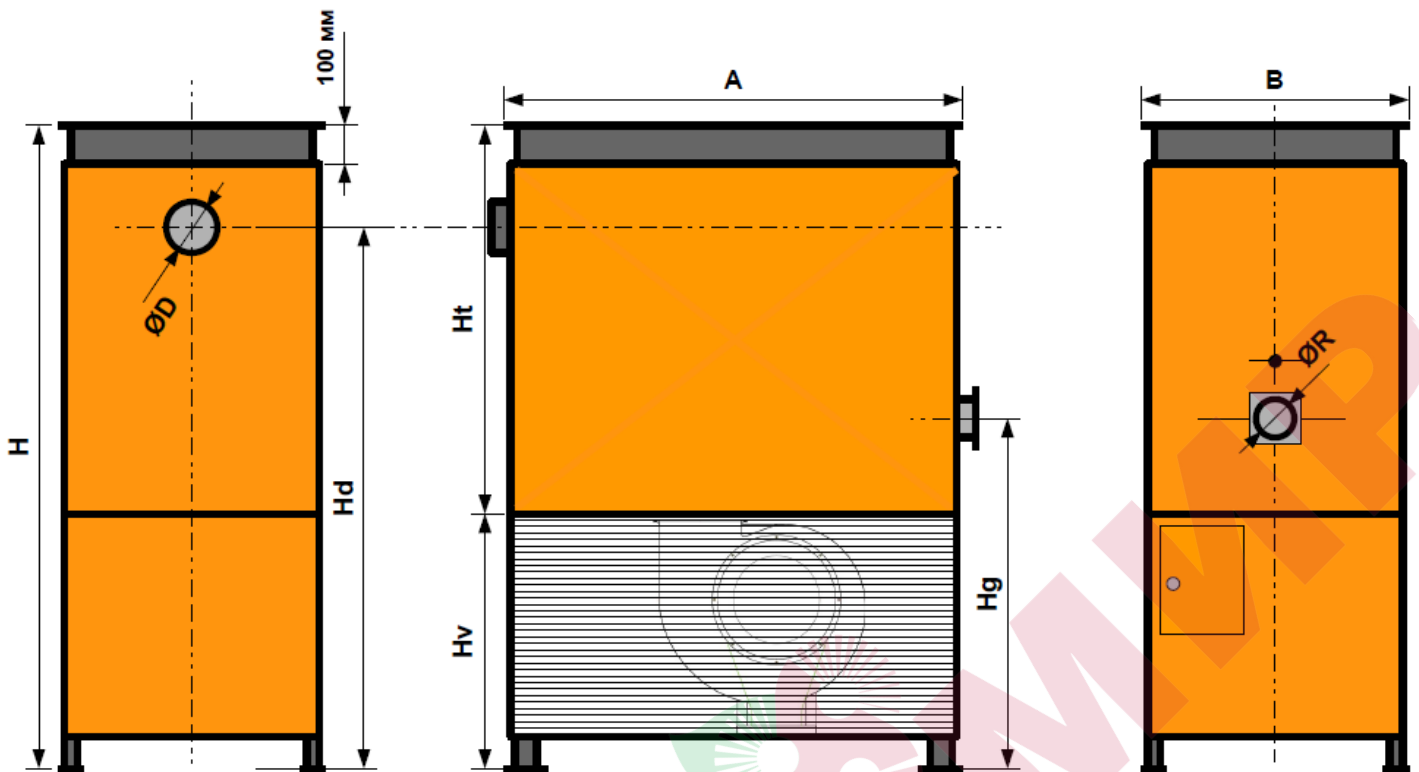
Габаритные размеры воздухонагревателей серий VT-K
